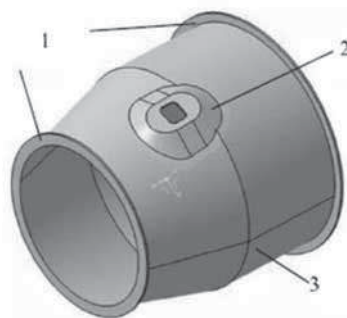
Базовая форма внешнего контура корпуса двигателя [51]:
